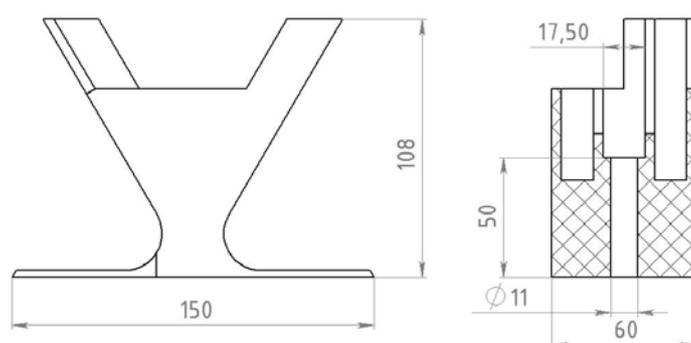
Внешний вид и габаритные размеры УКК2-60 (мм)
